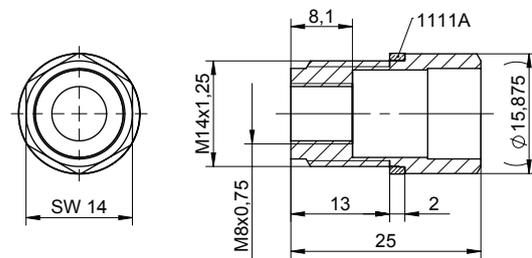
Adapter Typ 6589Q01. Sensor frontbündig
